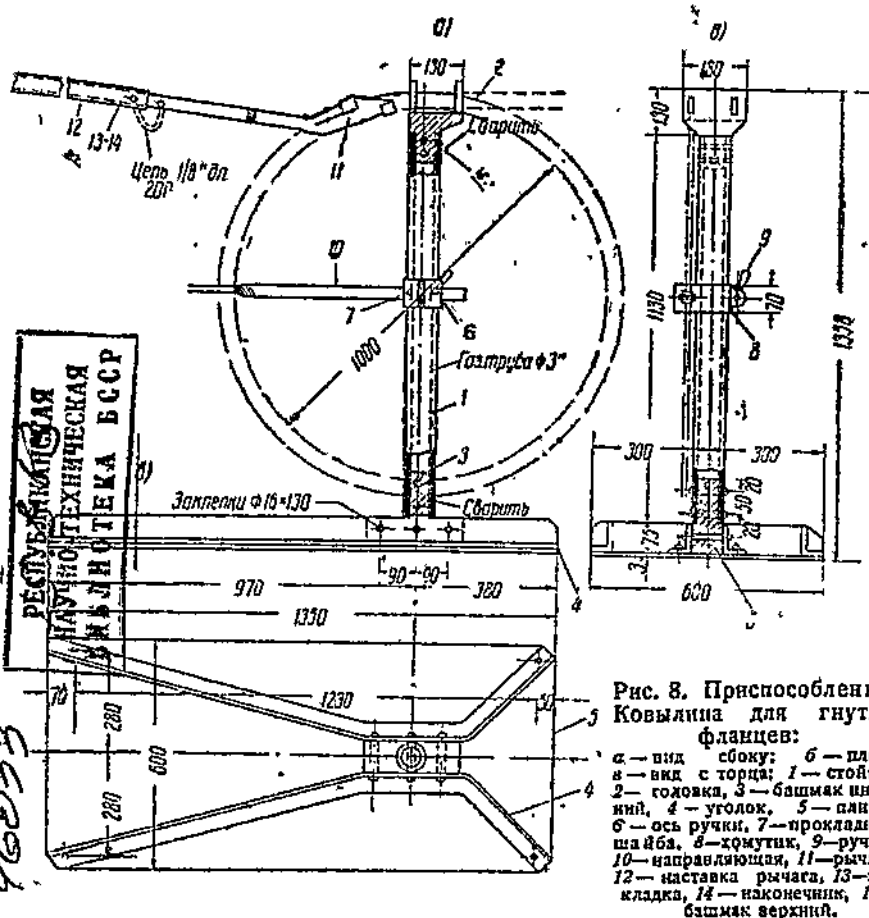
Приспособление Ковылина для гнутья фланцев:
